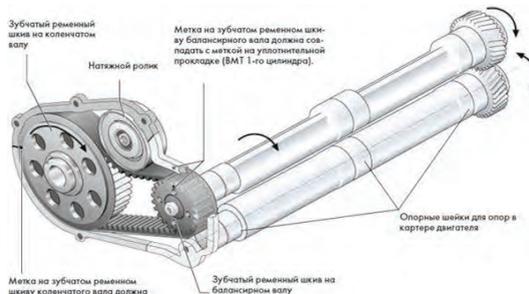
Ременно - шестеренчатый привод балансирных валов.
